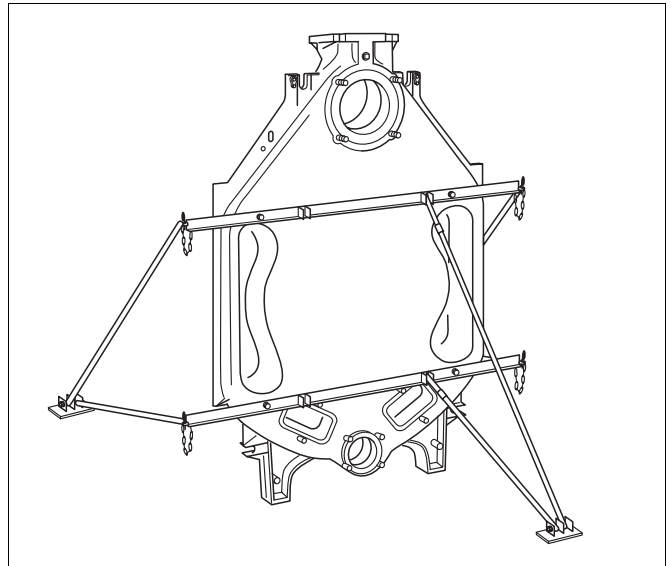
Fissaggio del dispositivo di montaggio ausiliario
